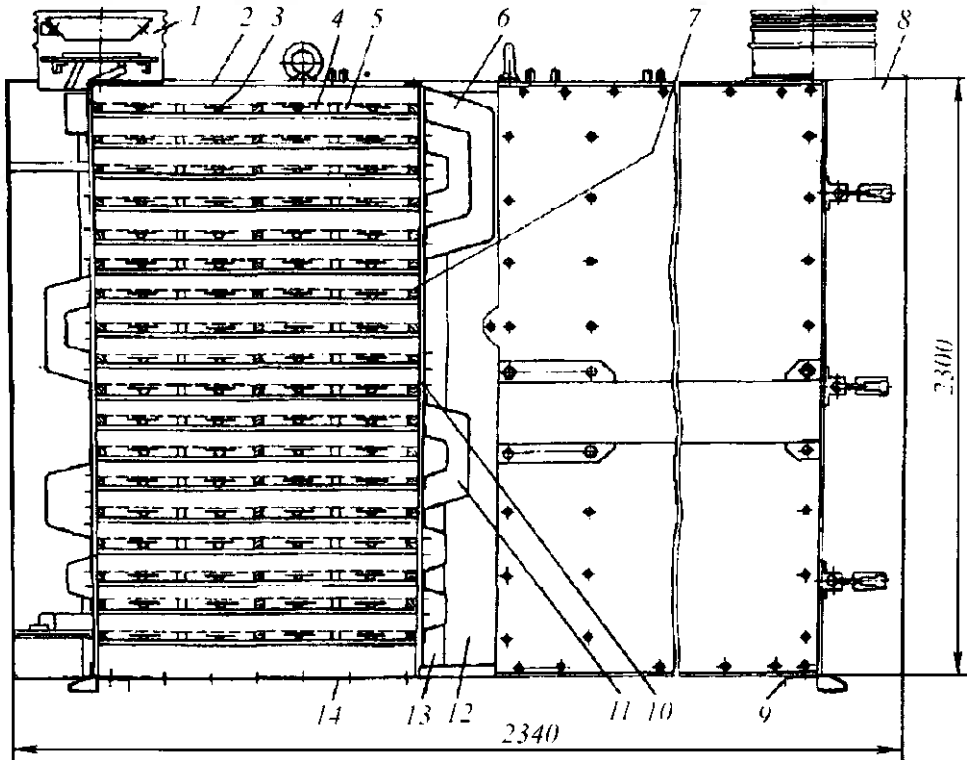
Шкаф рессева ЗРШ4-4М
